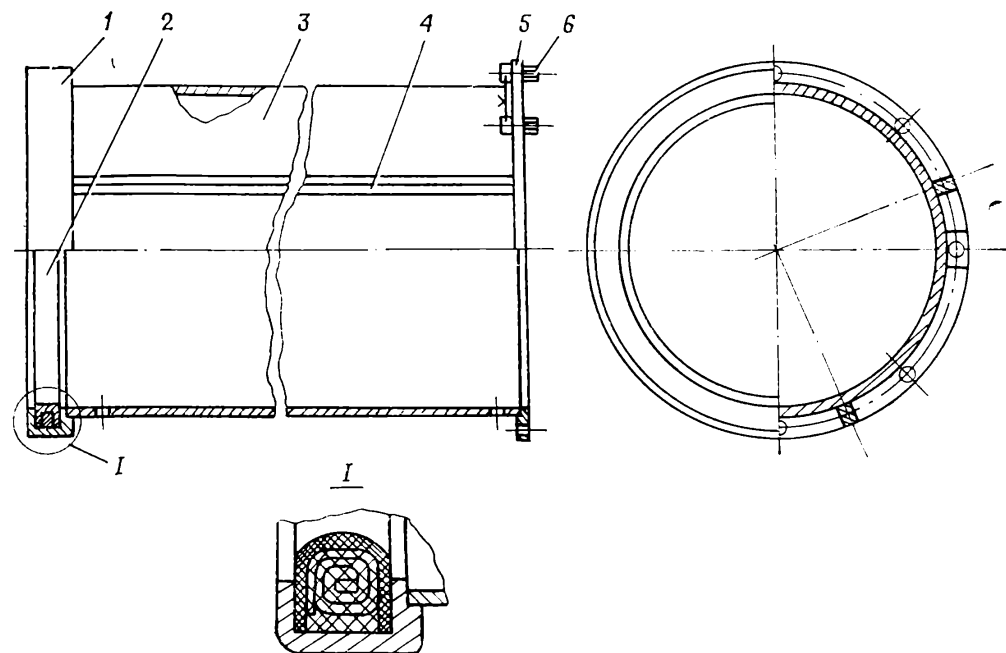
Установка приспособления 41.140 для оттягивания ствола:
